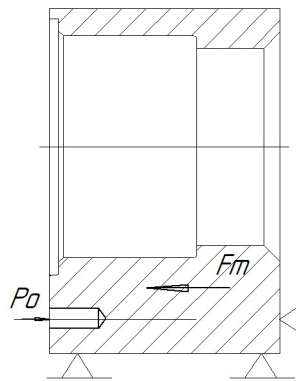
Схема дії сил та базування при закріпленні заготовки для деталі «Стойка А221.03»
